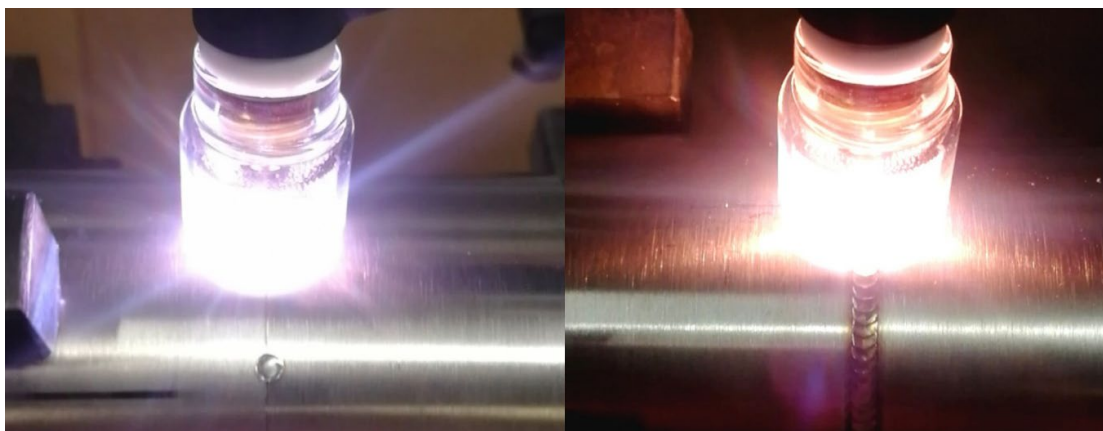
Сварка прихваточным швом трубы (слева), изготовленной из кислотостойкой стали (316L), и точечная сварка с использованием серии функции MicroTack, которая напоминает импульсную сварку, на поворотном устройстве (справа).
